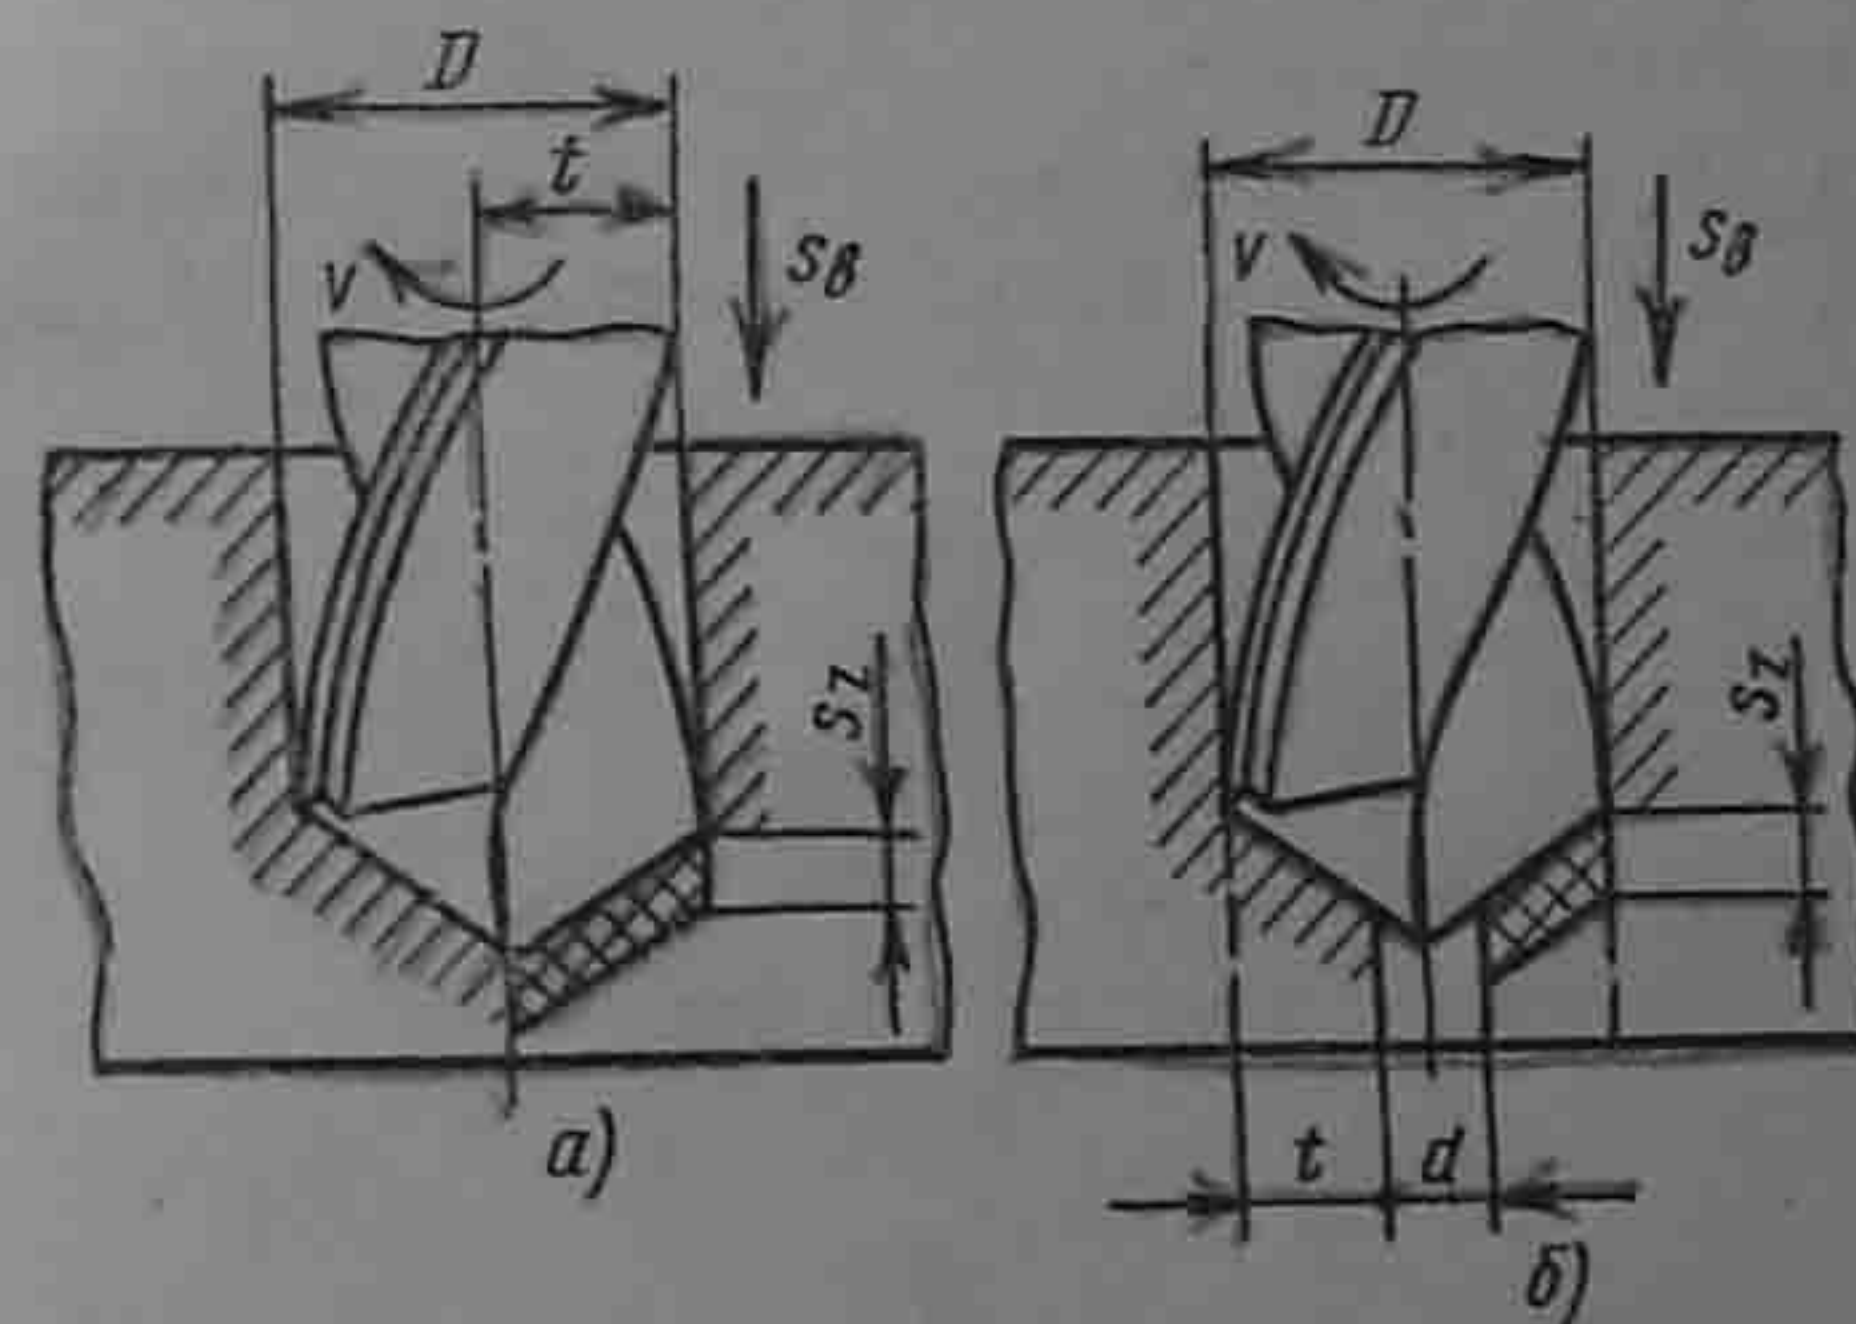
Схемы сверления (a) и рассверливания (б)
